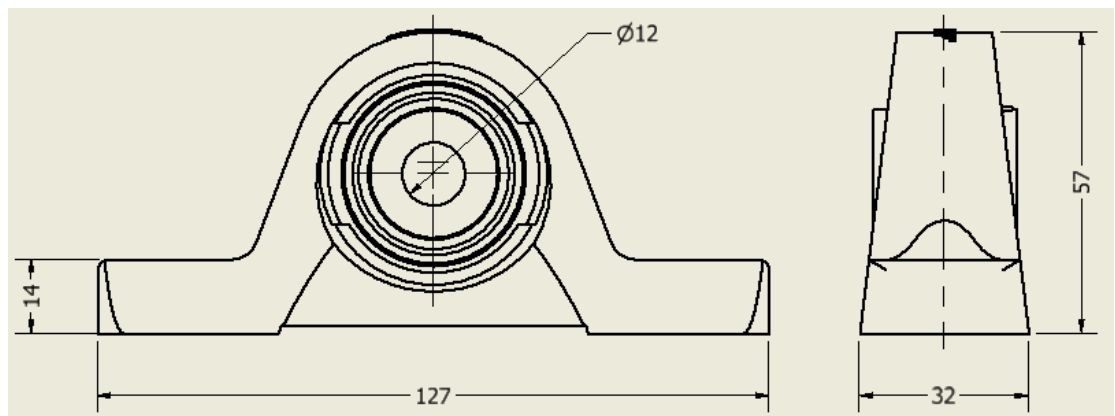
Soporte de pie con rodamientos de bola SY12
